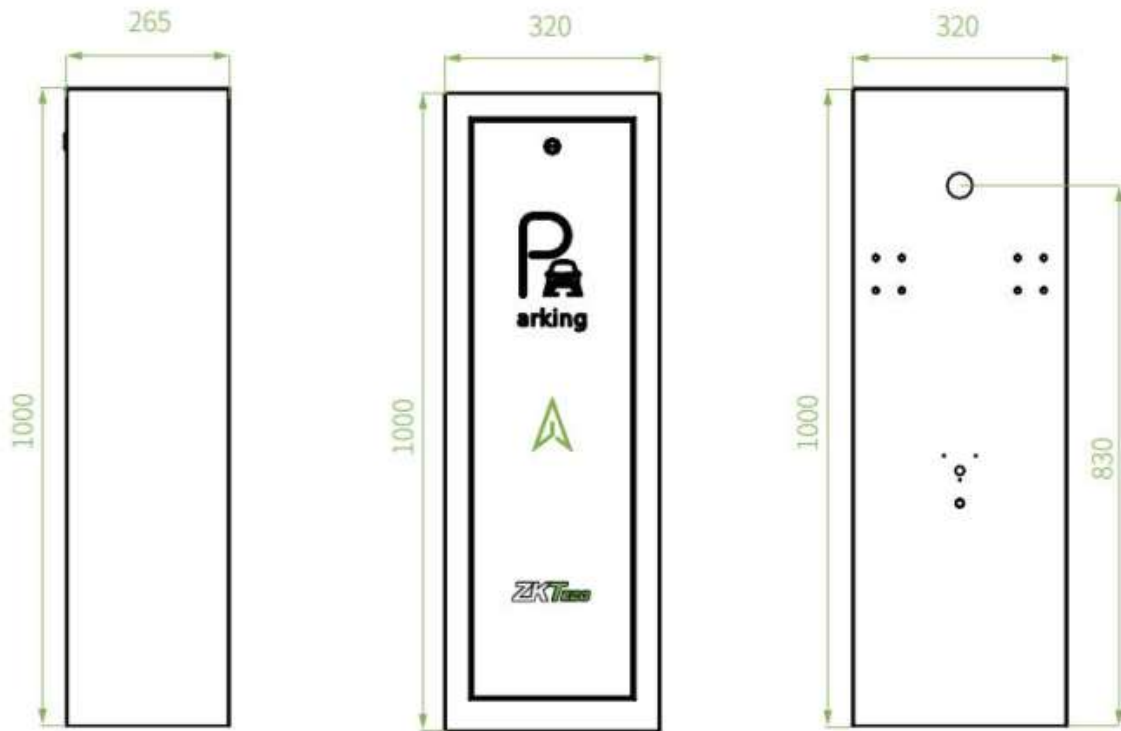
Габаритные размеры корпуса шлагбаума (в мм)
